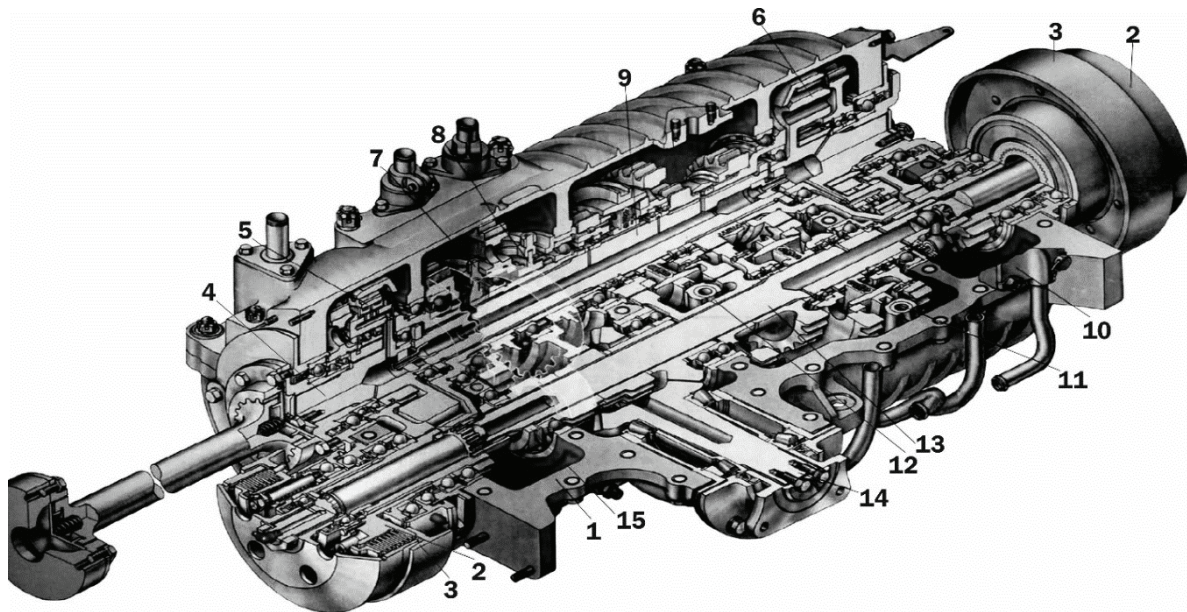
Главная передача МТ-ЛБ: 1 — картер с крышкой; 2 — фрикционы механизмов поворота; 3 — тормоза механизмов поворота; 4 — ось промежуточной шестерни заднего хода; 5 — промежуточная шестерня заднего хода; 6 — планетарные ряды механизмов поворота; 7 — вилка включения заднего хода; 8 — вилка включения I и II передач; 9 — главный вал; 10 — фильтр очистки масла; 11 — вилка переключения V и VI передач; 12 — вилка переключения III и IV передач; 13 — передаточный вал; 14 — первичный вал; 15 — муфта
